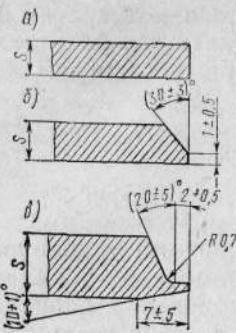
Форма и размеры подготовки кромок труб и деталей при односторонней сварке
